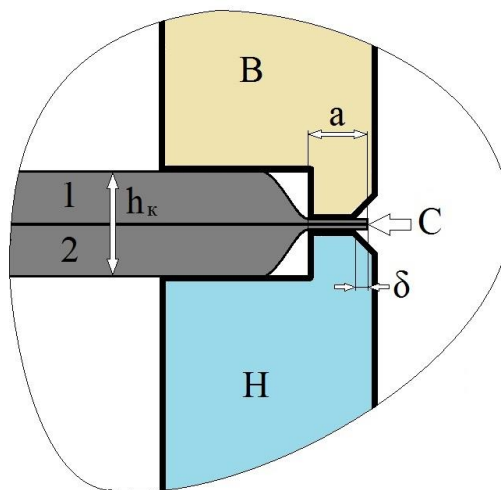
Геометрия приспособления для обжима свариваемых пластин: В – верхний элемент приспособления; Н – нижний элемент; С – сварной шов; 1 и 2 – свариваемые в конверт пластины; h_k – высота конверта; a – ширина сварочной полки; δ – выступ полки
